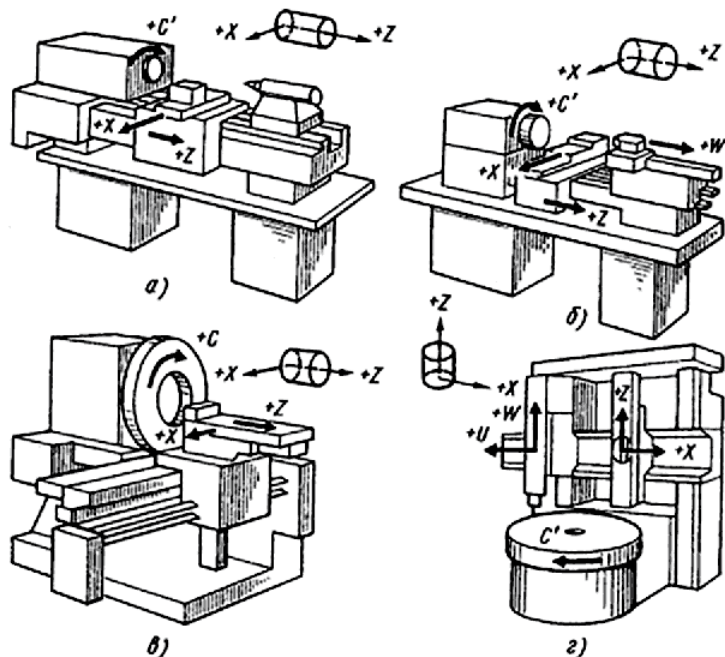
Обозначение осей координат и положительных направлений движения на токарных станках с ЧПУ
